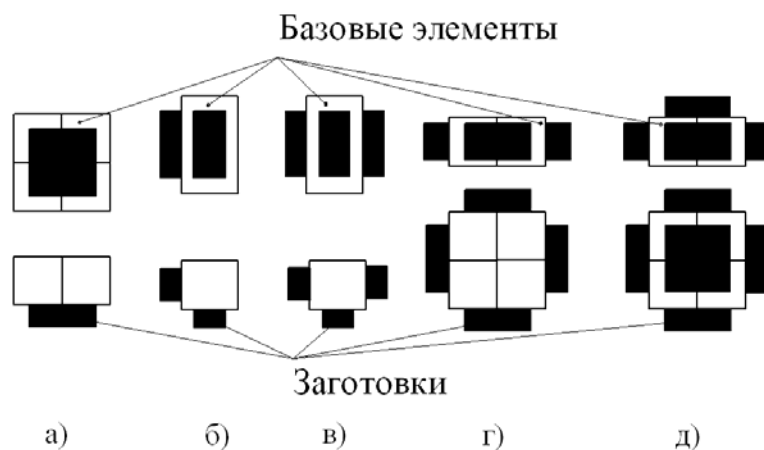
Схемы базирования и закрепления заготовок на базовых модулях
